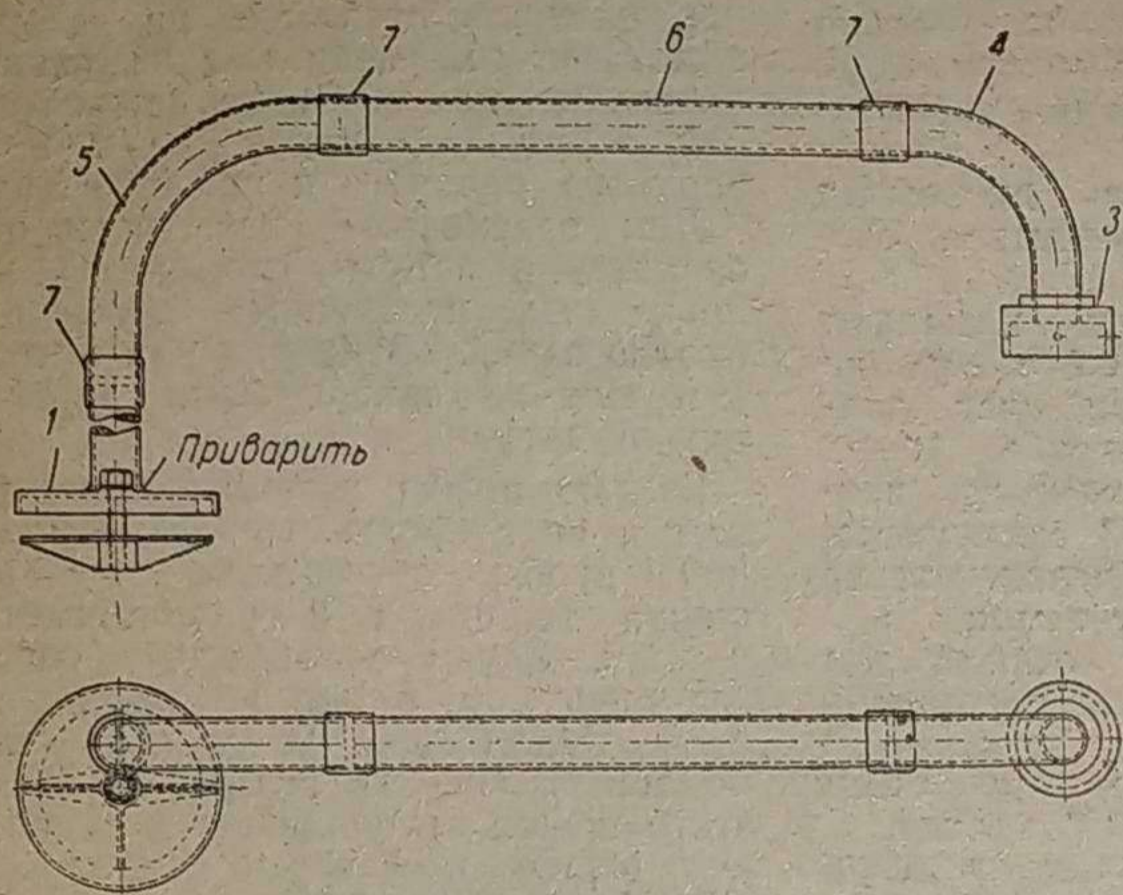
Приспособление для проверки герметичности газогенераторной установки
